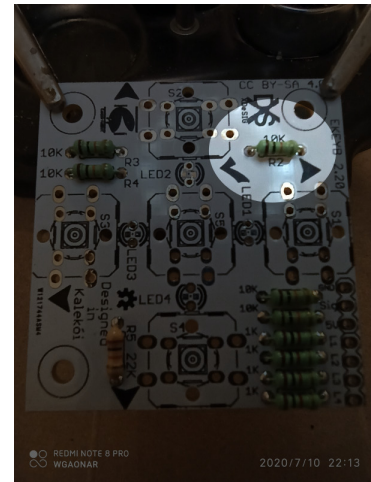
Soldadura de las resistencias en la botonera parte 1.
